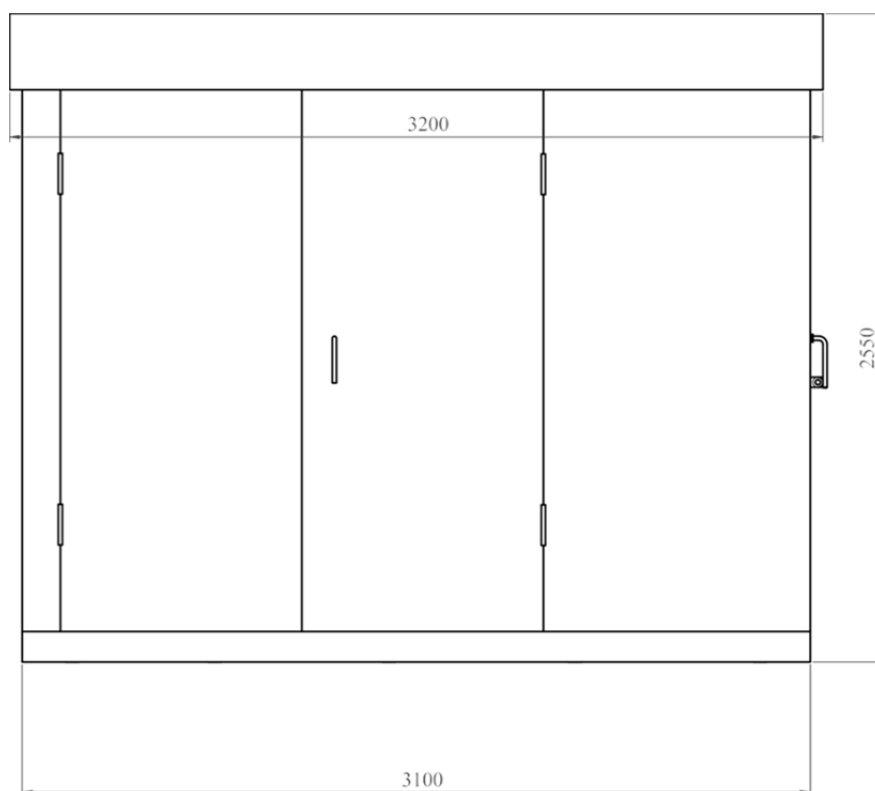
Внешний вид и габаритные размеры КТПН – 100 кВА
